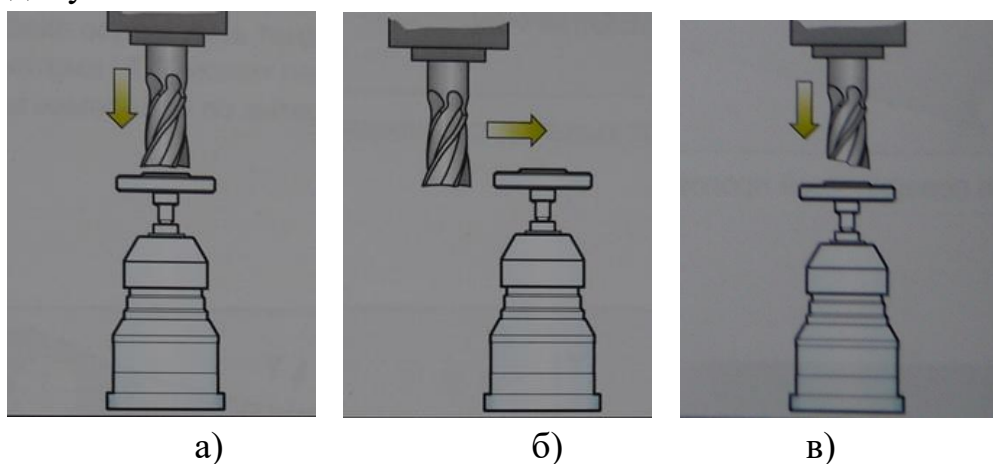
Принципова схема вимірювання інструменту на верстаті:
